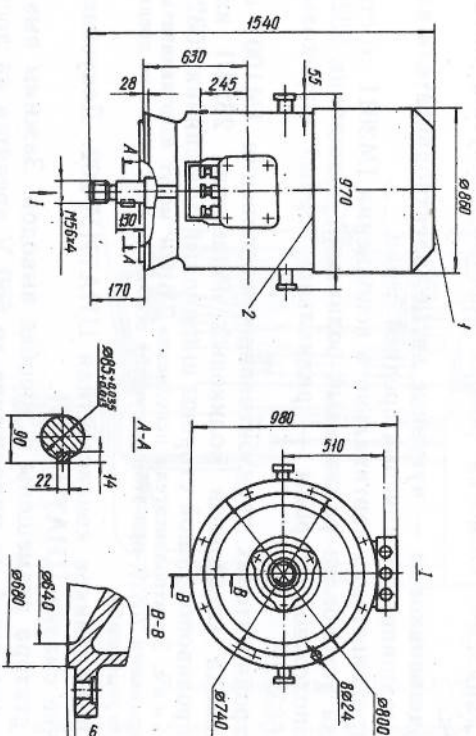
Габаритные, установочные, присоединительные размеры электродвигателя АОЗ-400М-10/120М4. Масса электродвигателя — 2100 кг. 1 — вход воздуха; 2 — выход воздуха
